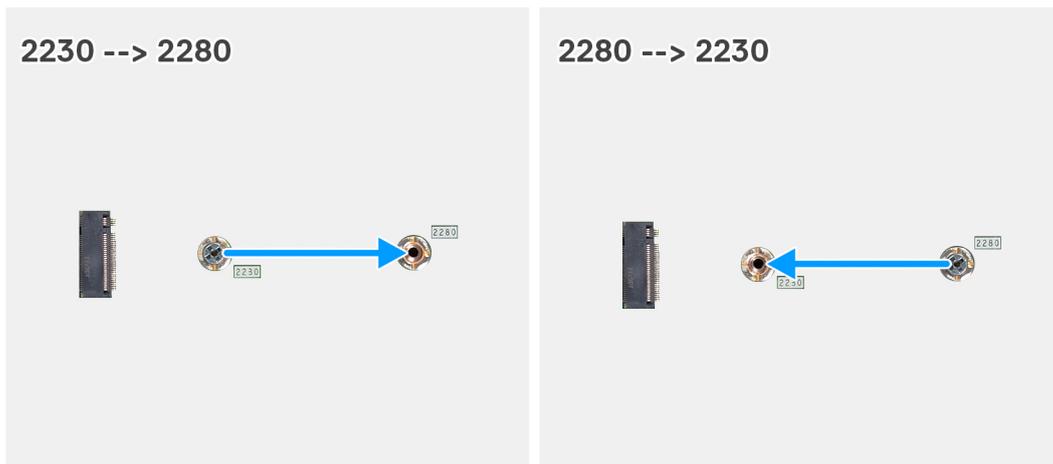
Verschieben der Solid-State-Schraubbefestigung auf M.2-Steckplatz 0
